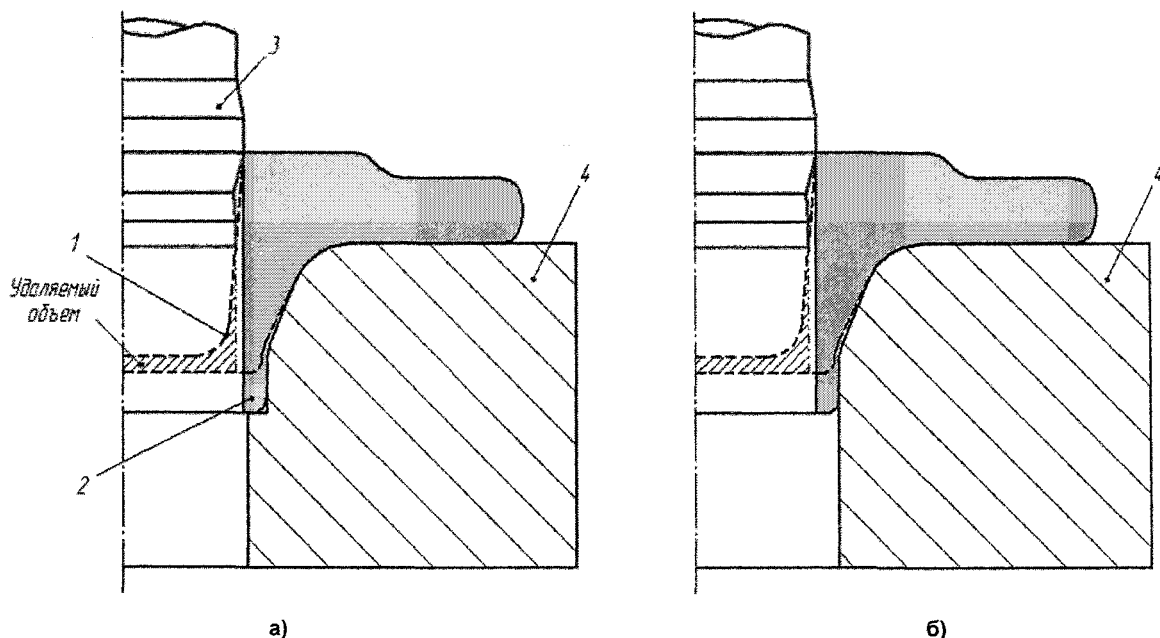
Схема деформации прошивка-раздача-выдавливание/вытяжка-калибровка (ПРВК): а - с закрытой прошивной матрицей; б - с открытой прошивной матрицей; 1 - контур предварительной поковки; 2 - окончательная поковка; 3 - пуансон комбинированный; 4 - матрица прошивная
